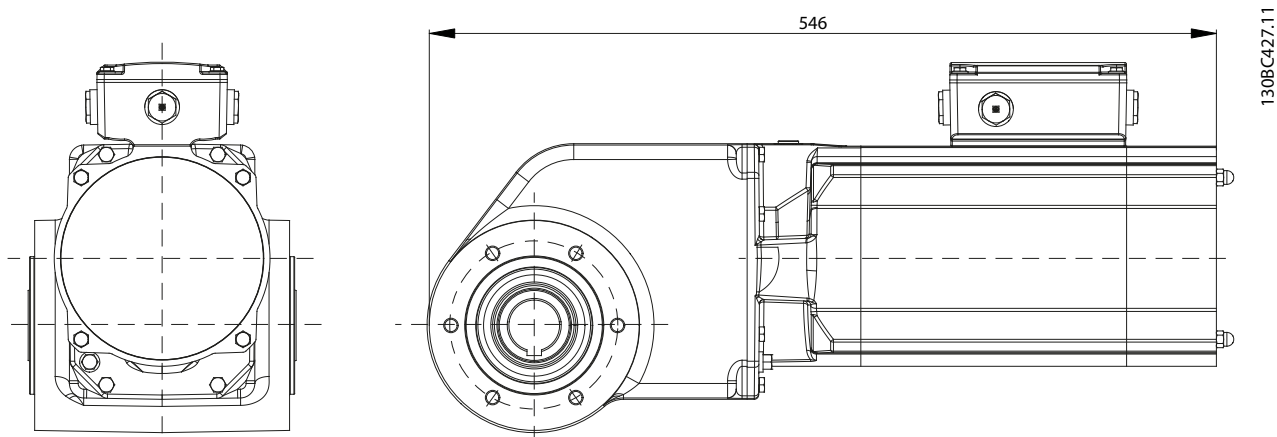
Dimensiones: OneGearDrive con opción de freno mecánico
